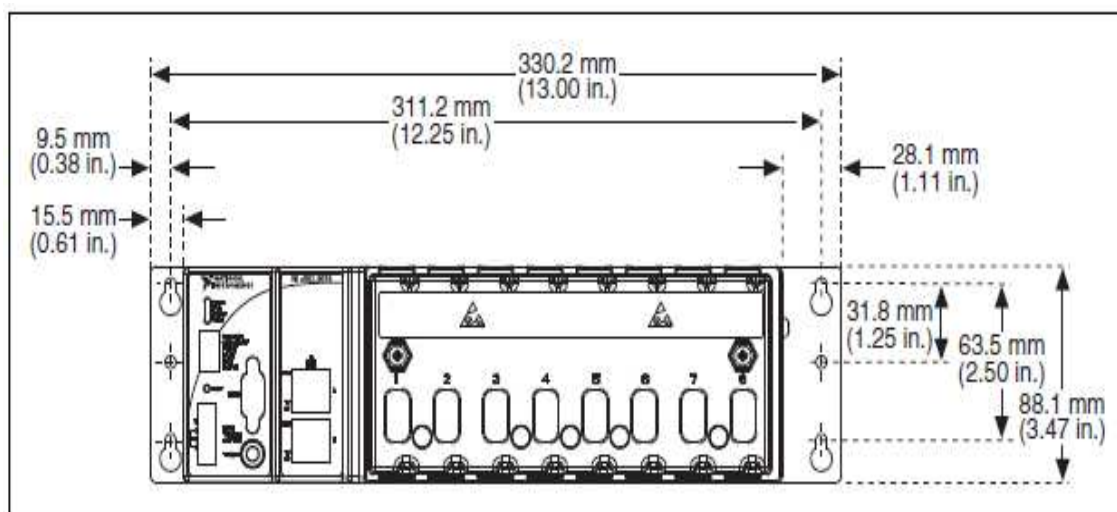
Panel con Accesorios Instalados y Dimensiones del cRIO-9074
